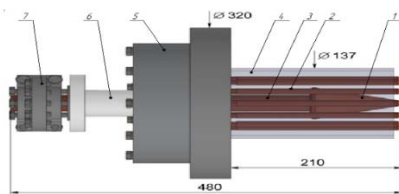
Газоразрядный магнитоплазменный компрессор:
